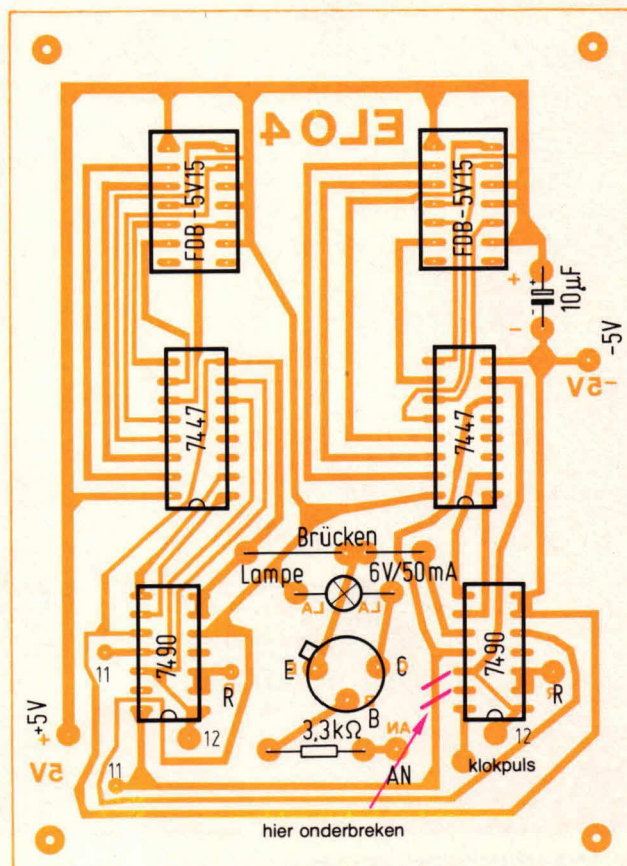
Gedrukt bedradingspaneeltje voor de universele indicator met montageplan.
